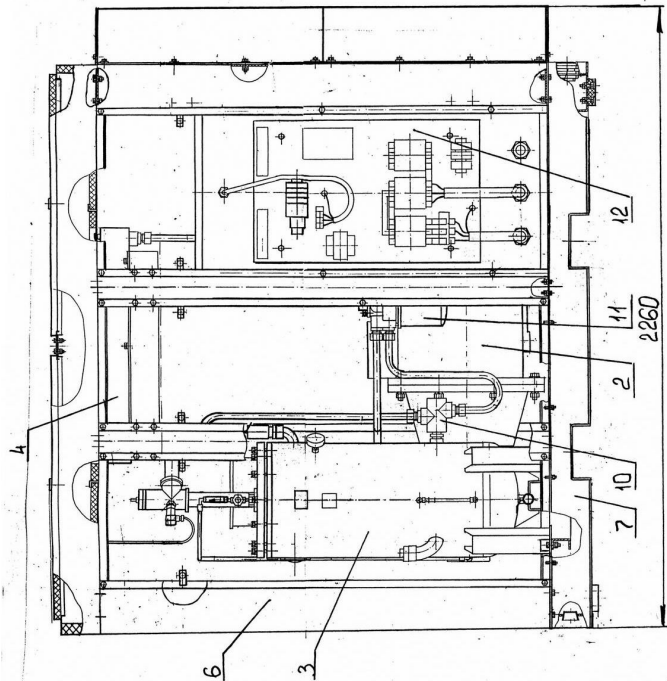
Установка компрессорная АСО-ВК-^{8,0}/₉ и АСО-ВК-¹⁰/₉.
